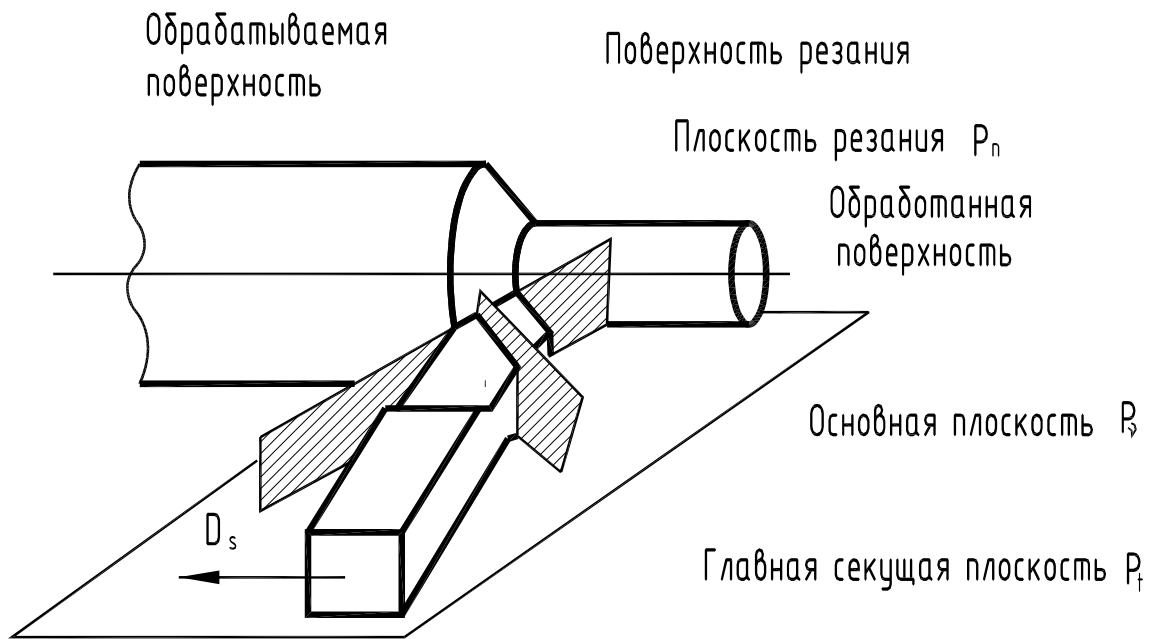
Схематическое изображение поверхностей заготовки и координатных плоскостей
